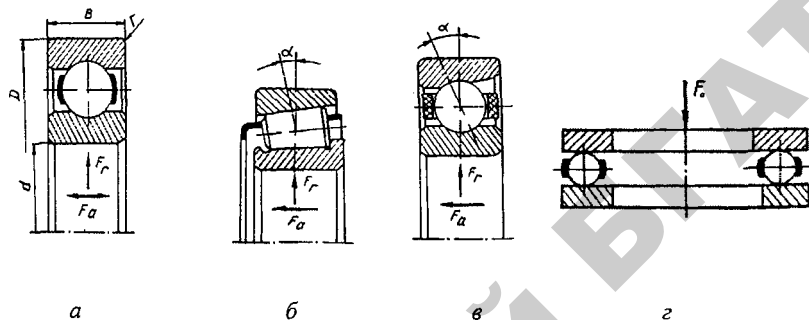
Подшипники качения: а – шариковый радиальный; б – конический радиально-упорный; в – радиально-упорный шариковый; з – упорный шариковый
